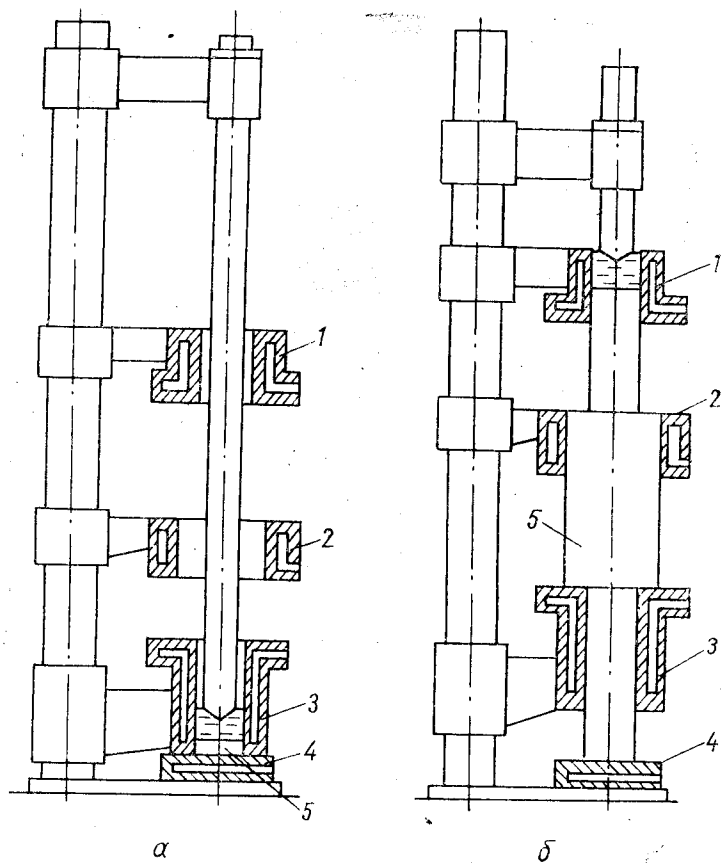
Схема виливання заготовки прокатного вала електрошлаковим литтям на початковій (а) та кінцевій (б) стадіях:
